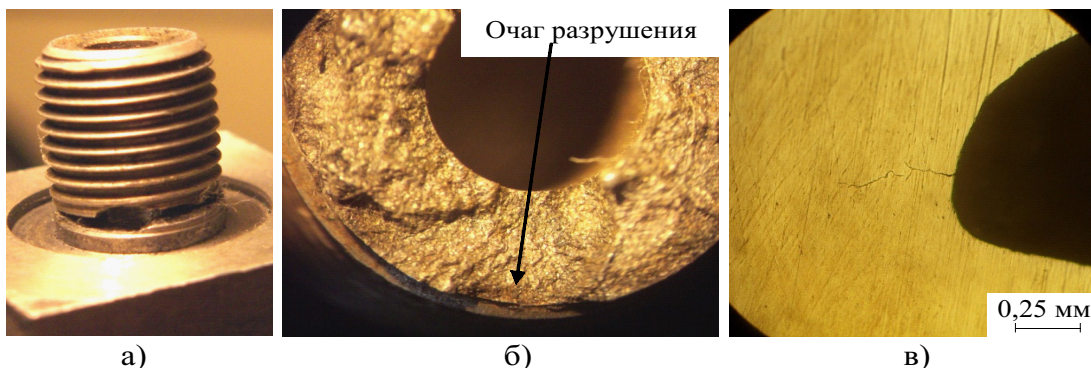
Отломившаяся резьбовая часть переходного штуцера манометра (а) и расположение очага разрушения резьбовой части штуцера (б); в – трещины в резьбовой части переходного штуцера
